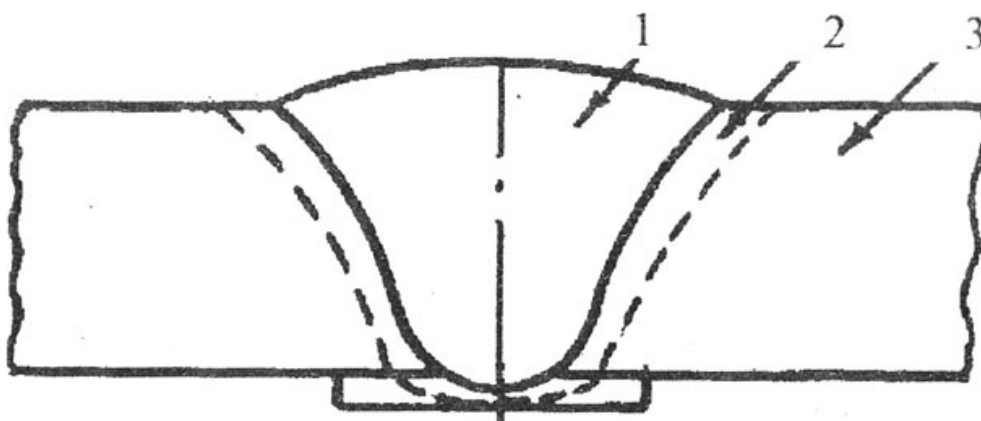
Основні ділянки мікрошліфа поперечного зразка зварного з'єднання:
